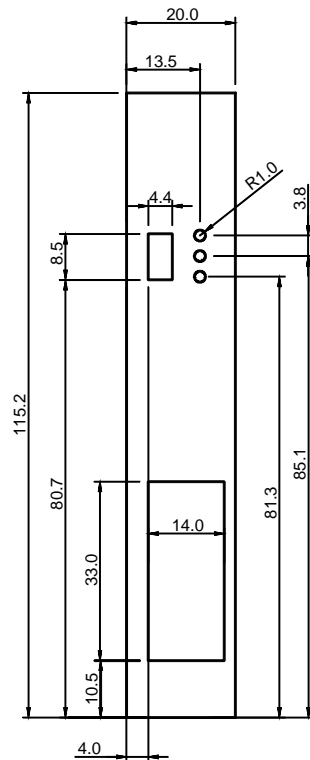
Abmessungen Frontblende für CIFX 80-RE
